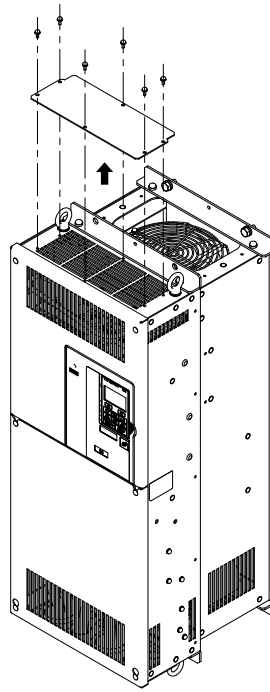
Remova a tampa de proteção superior (2A0143 a 2A0273 e 4A0124 a 4A0302)
